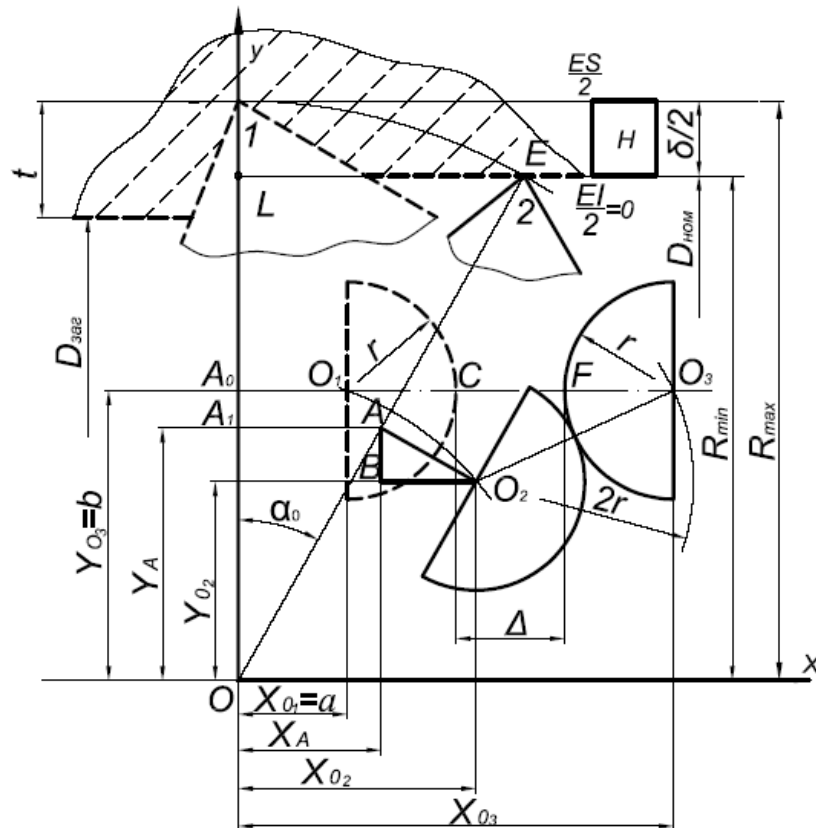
Розрахункова схема для визначення величини зазору Δ між упорними і регулювальними гвинтами прогресивної дворіцевої розточувальної головки:
